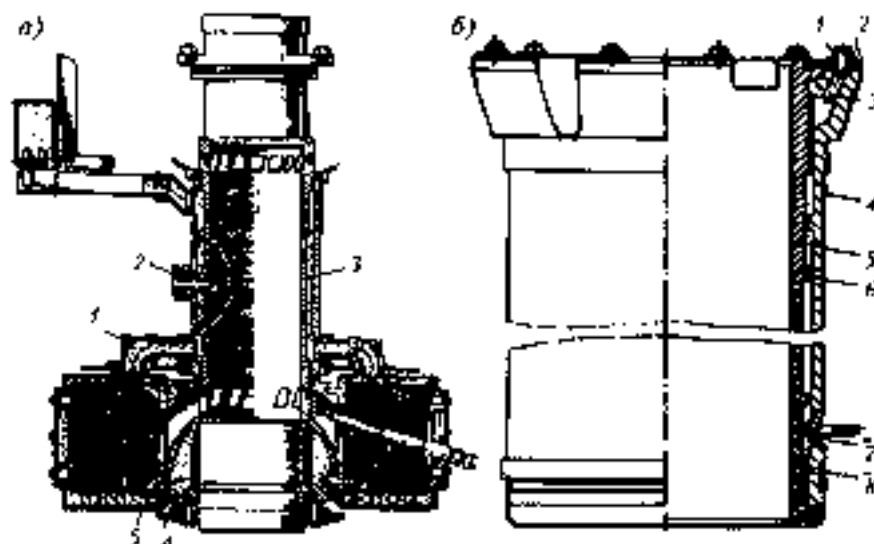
Циліндрово-водяний металовиток дизеля:
